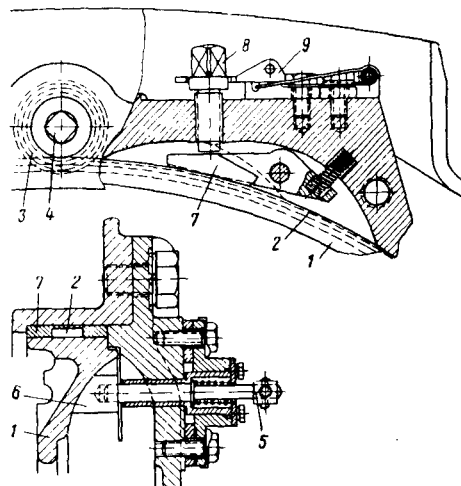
Щёткодержатели коллекторных двигателей типов: а—ELM-670; б—16WB-880
